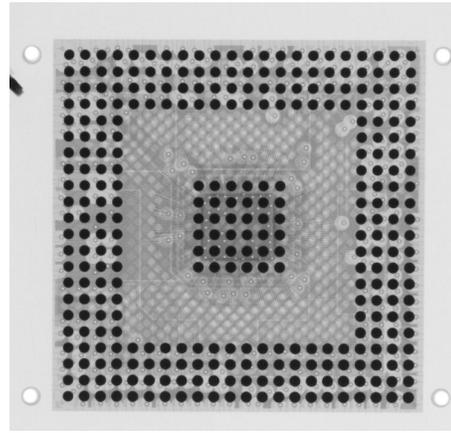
Radiografía del chip BGA de 324 bolitas, soldado en la placa de pruebas.
